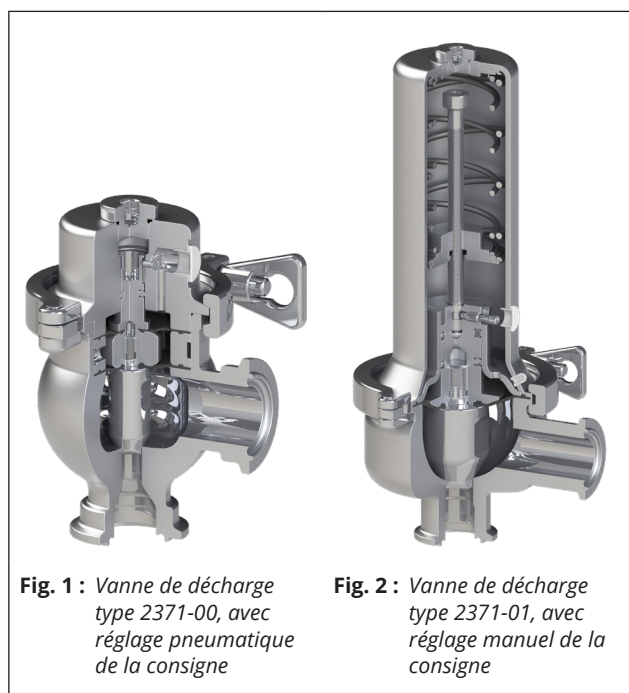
Vanne de décharge type 2371-00, avec réglage pneumatique de la consigne
